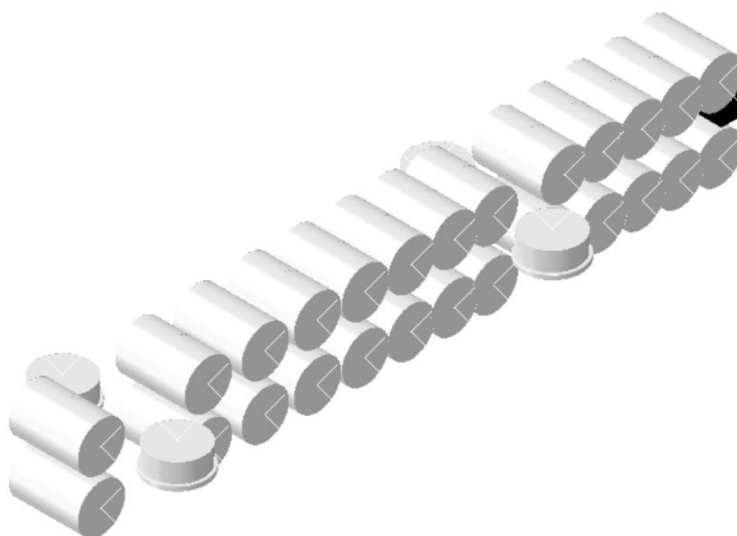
Розрахункова схема 3D-моделі прокатки на стані з еджерними валками
